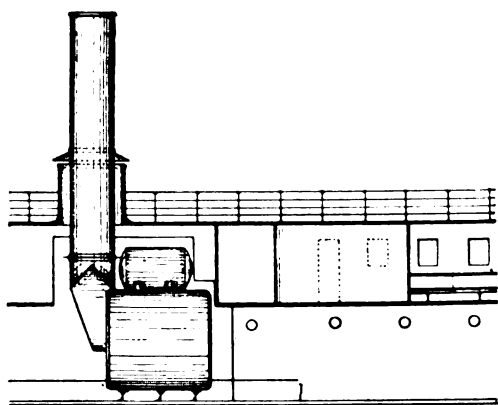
Schnitt durch den Maschinenraum und Ansicht des Kessels.
